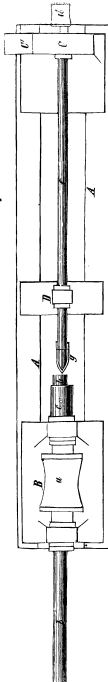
Neue Anordnung eines Werkzeuges zum Bohren langer Löcher in Holz. Geandert.
